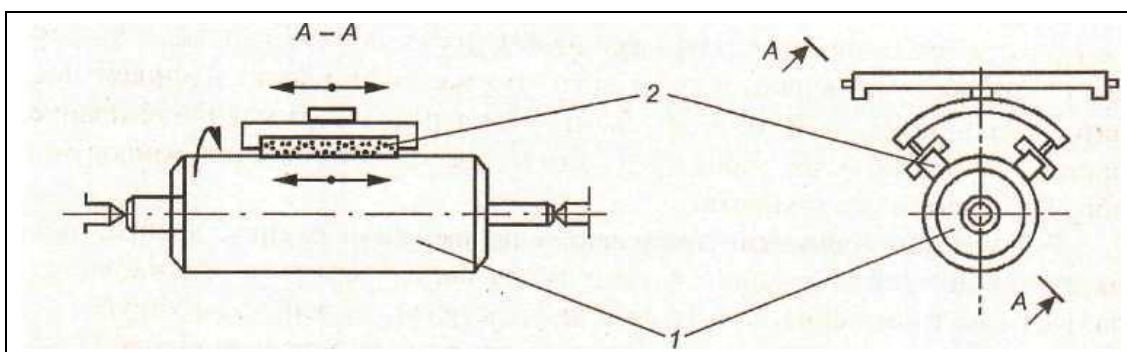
Схемы движений заготовки и инструмента при суперфинишировании: 1 -заготовка; 2 – инструмент.
